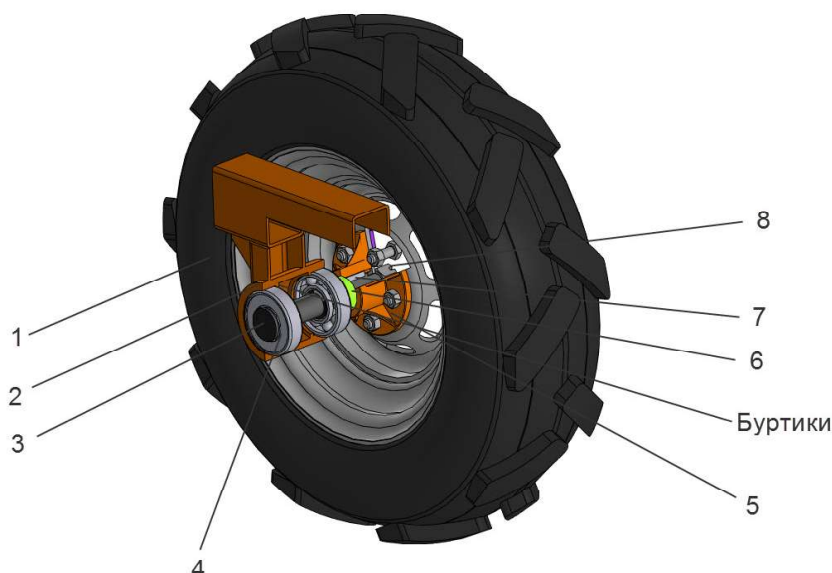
Трехмерная модель опорного колеса сажалки луковых культур:
